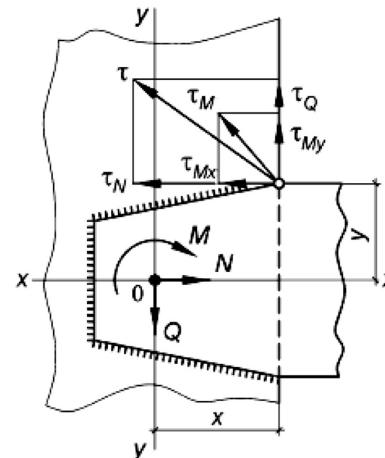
Розрахункова схема зварного з'єднання з кутовими швами [5, рис. 16.5]
